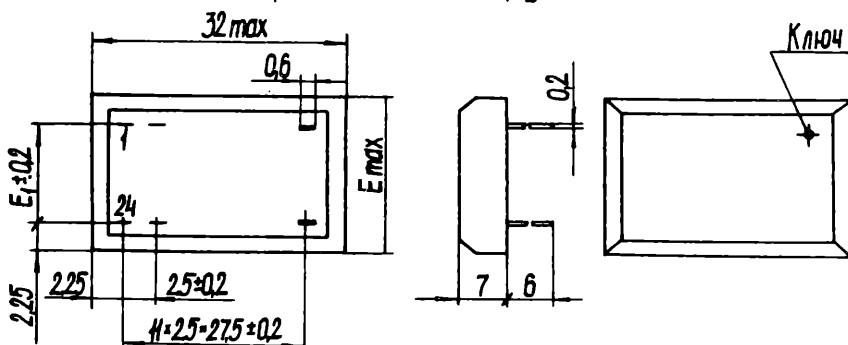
Керамикополимерный корпус ТЗ4.877.060
